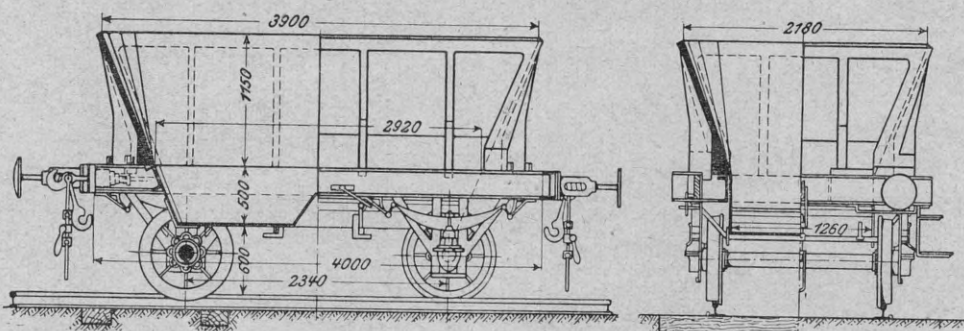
und 2. Eisenbahn-Güterwagen mit Eisenbetonkasten.
